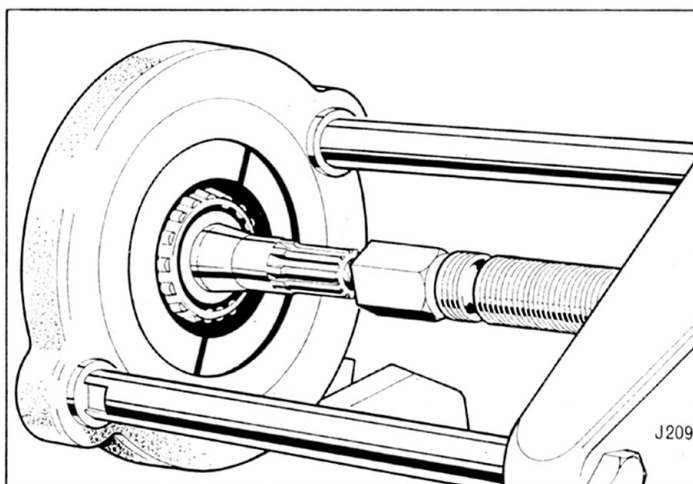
Extraction du roulement de tête de pignon d'attaque
